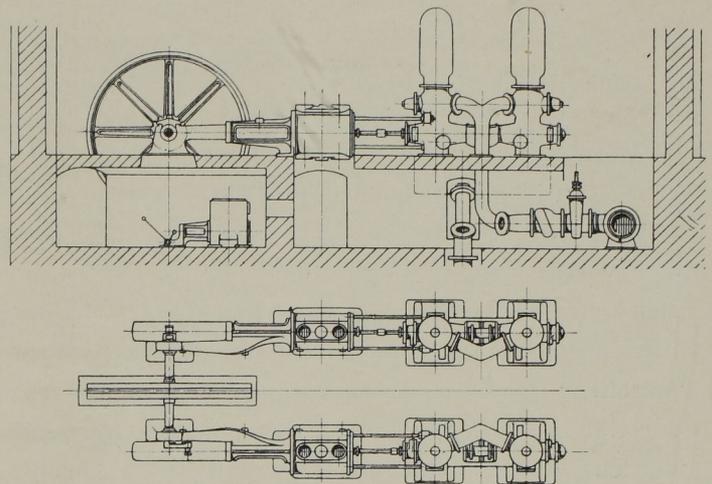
Seitenansicht und Grundriss der Maschine in Turin.
